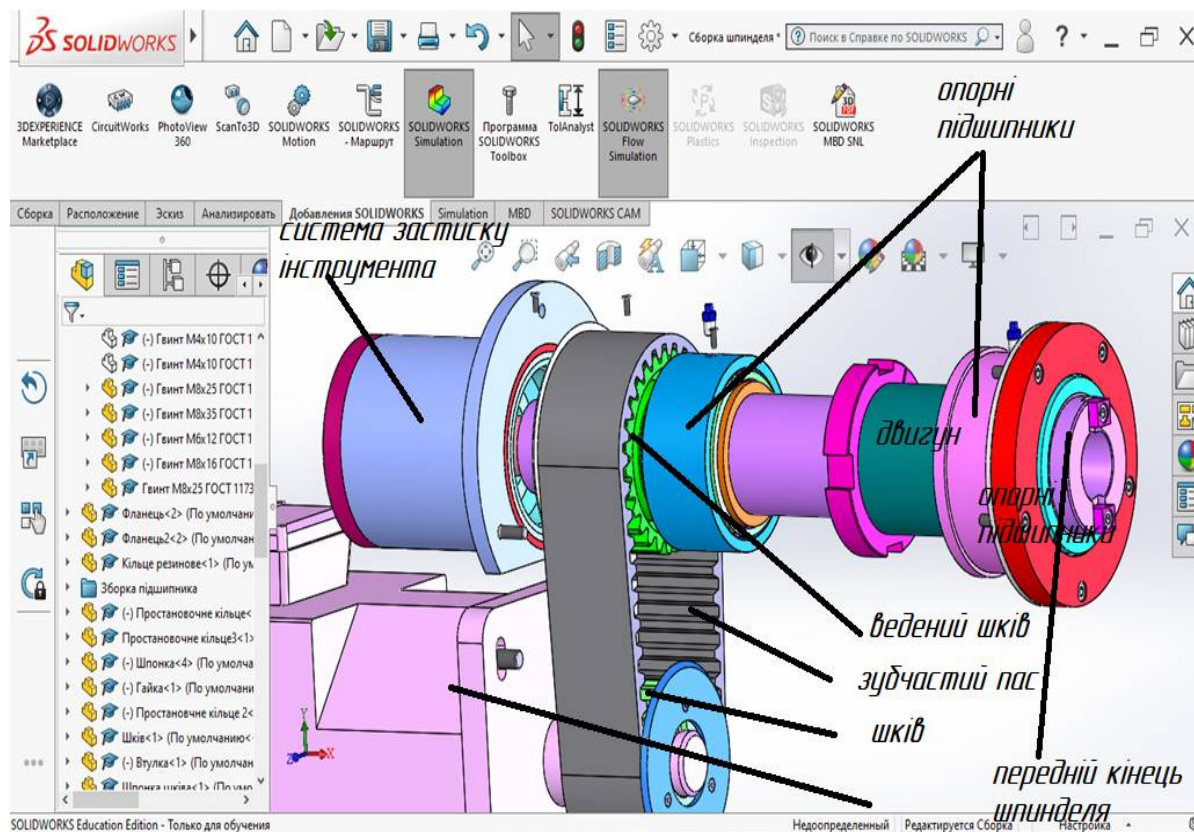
CAD-модель шпиндельного вузла вертикально-фрезерного верстата
